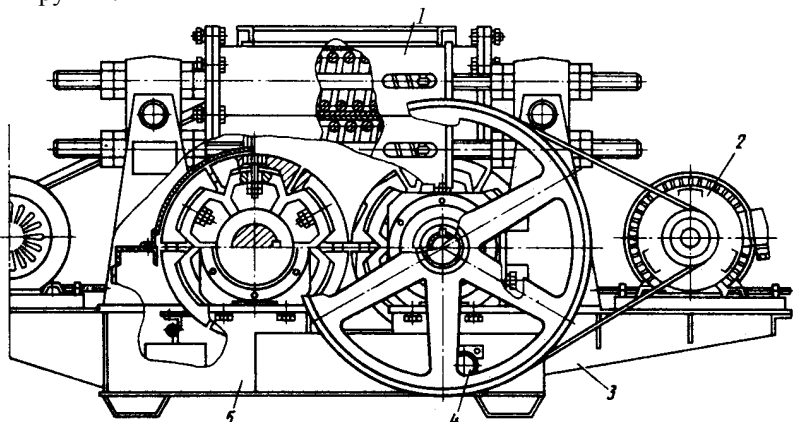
Двухвалковая дробилка с раздельным приводом валков.
